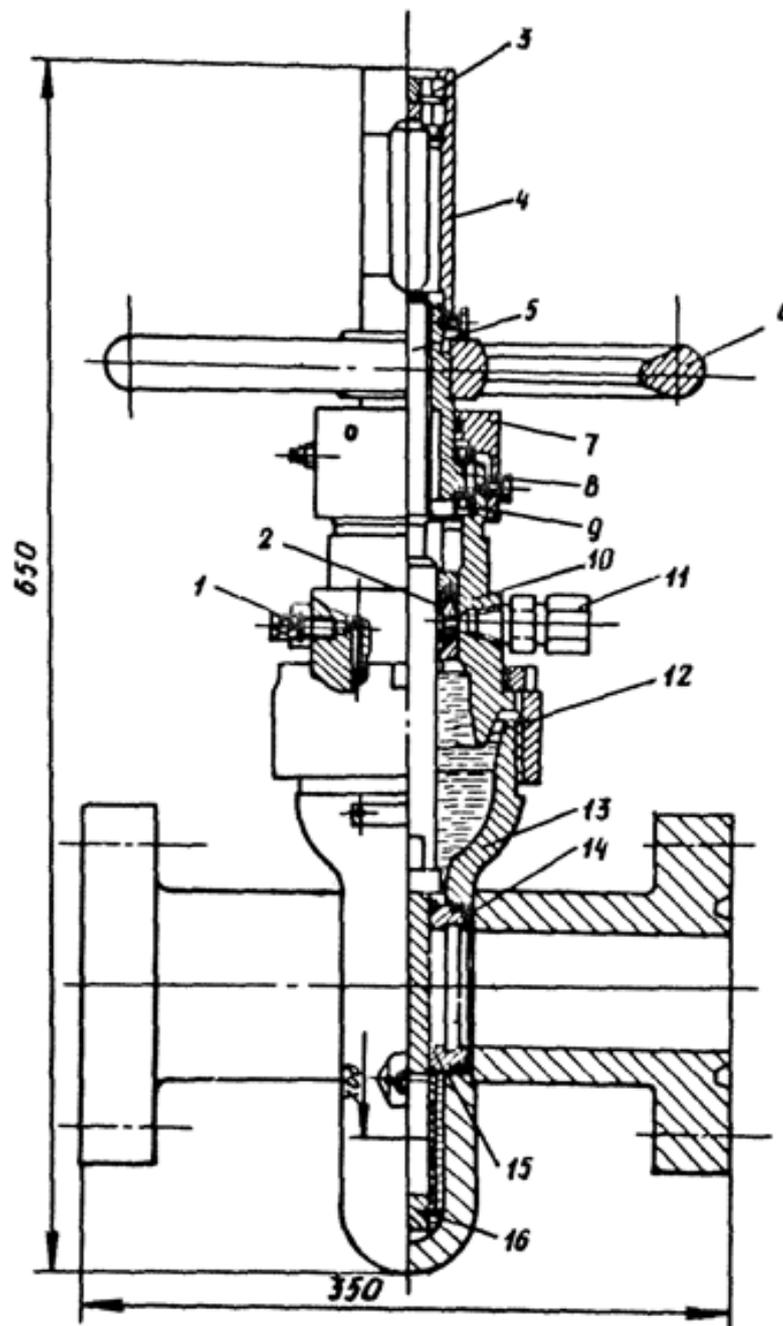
Задвижка типа ЗМ-65х21 с ручным приводом:
